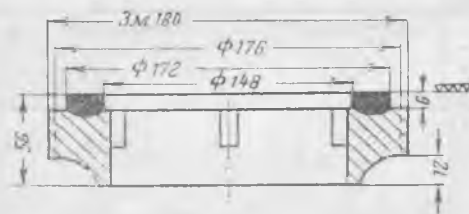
Окончательная заготовка уплотнительного кольца для вварки в корпус задвижки  $D_y = 200/150$  мм.
